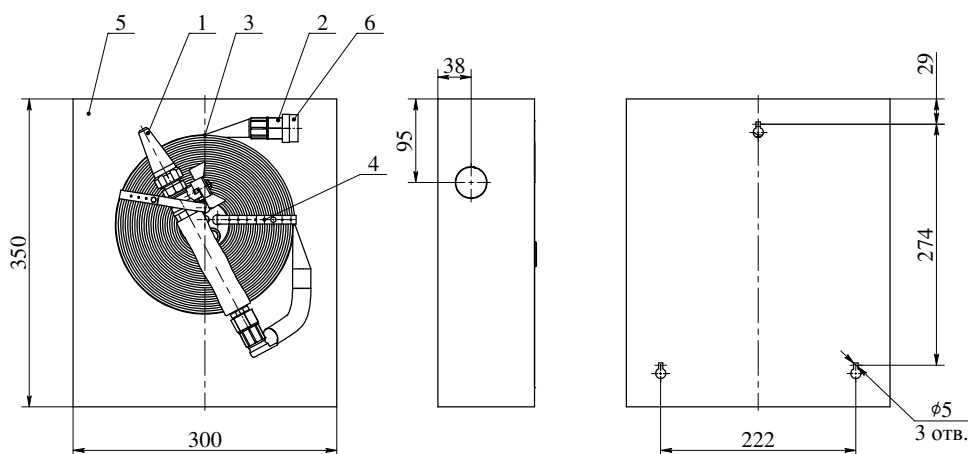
Габаритные и установочные размеры устройства в шкафу
